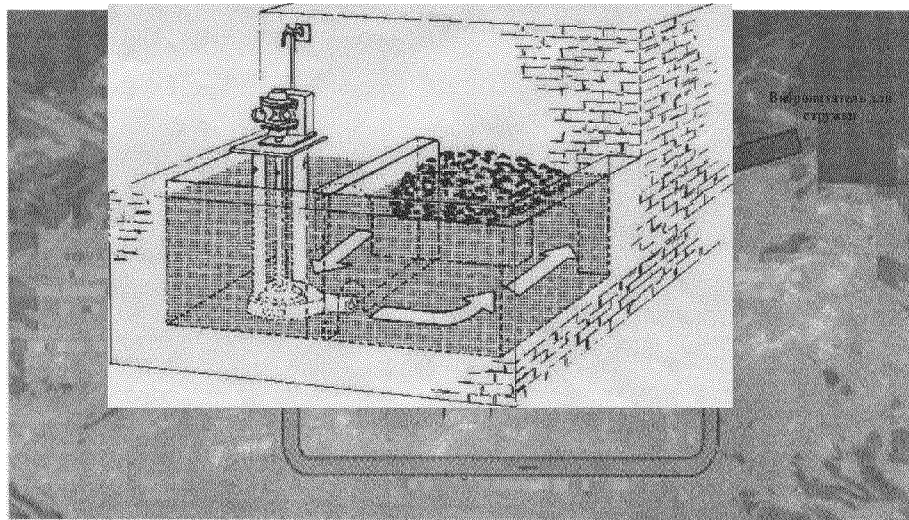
Схема процесу плавки металобрухту з розвиненою поверхнею за рахунок тепла розплаву, що циркулює під дією механічного насоса (The Carborundum Company Refractories & Electronics Division Metallurgies Branch)
